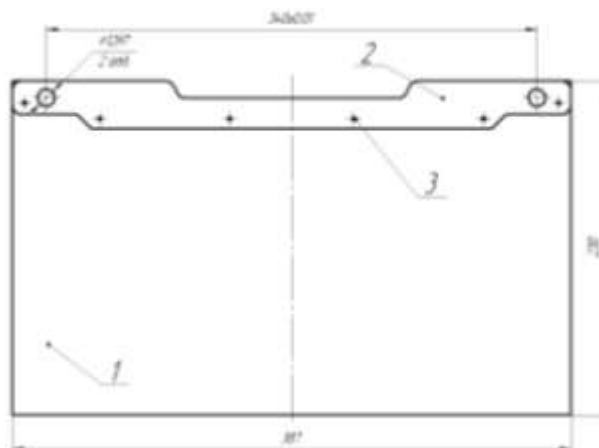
Крепление листа заготовки технологической оснастки к планке при помощи винтов:
